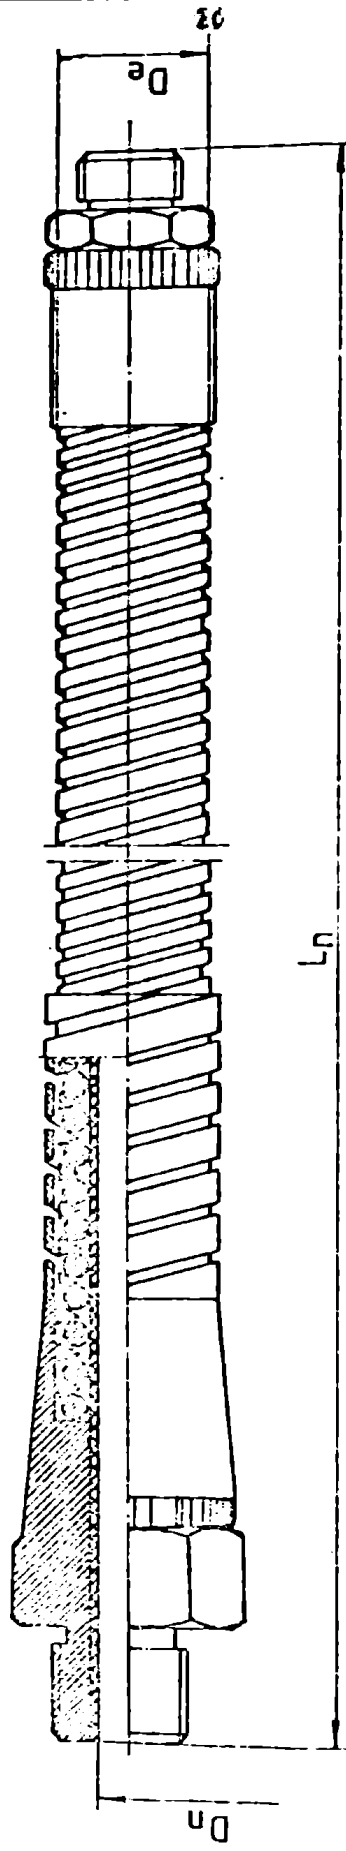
Tub flexibil cu remanență pentru susținerea elementelor de iluminat, tip FR.
